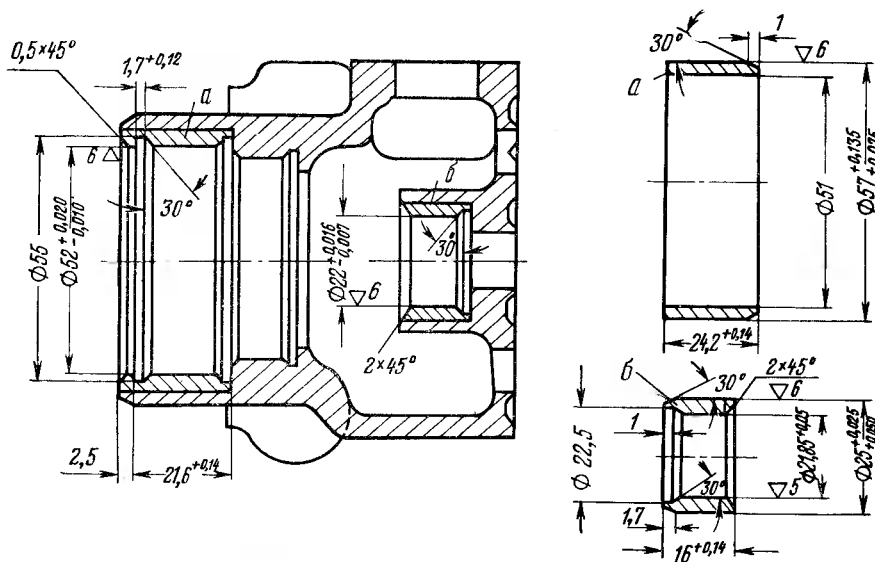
Ремонтные втулки корпуса насоса гидроусилителя рулевого управления:
